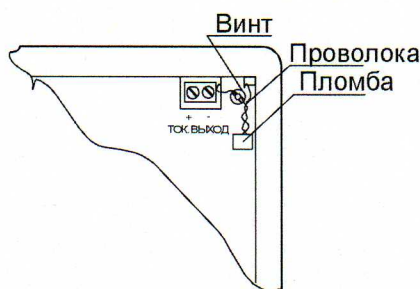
Схема пломбировки вторичного преобразователя при креплении в щит.
